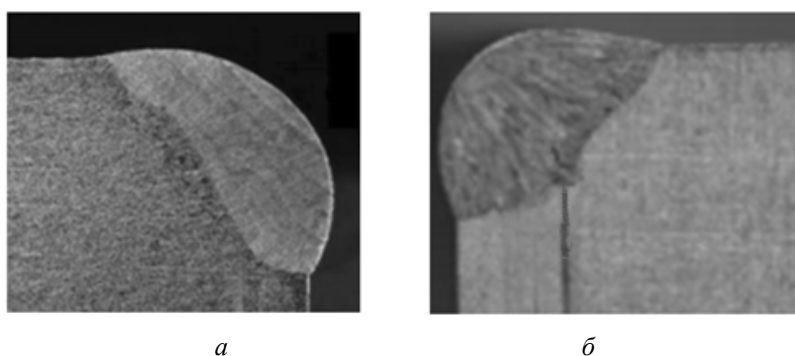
Наплыв на внутреннюю стенку сварного шва: а) лазерная сварка; б) сварка вольфрамовым электродом
